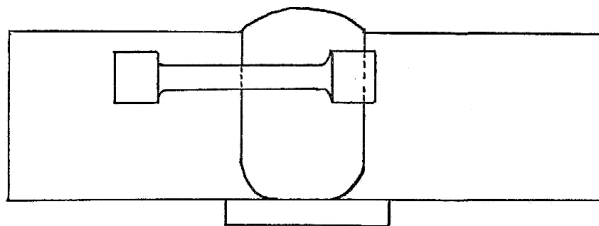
Схема вырезки образцов ролика рольганга на растяжение для исследования сварного соединения
